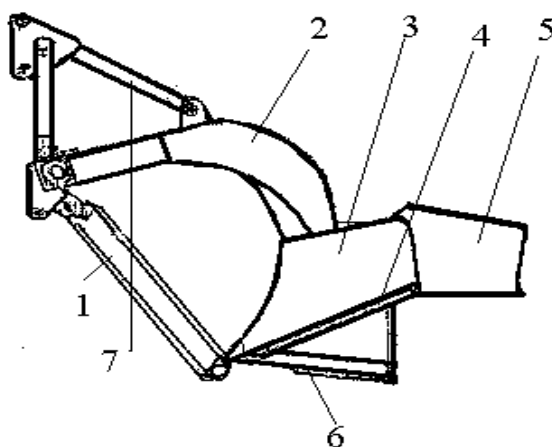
Плуг-канавокопатель ПКЛН-500: 1 – черенковый нож; 2 – остов; 3 – корпус; 4 – нож-откосник; 5 – бермоочиститель; 6 – опорная лыжа; 7 – навеска
